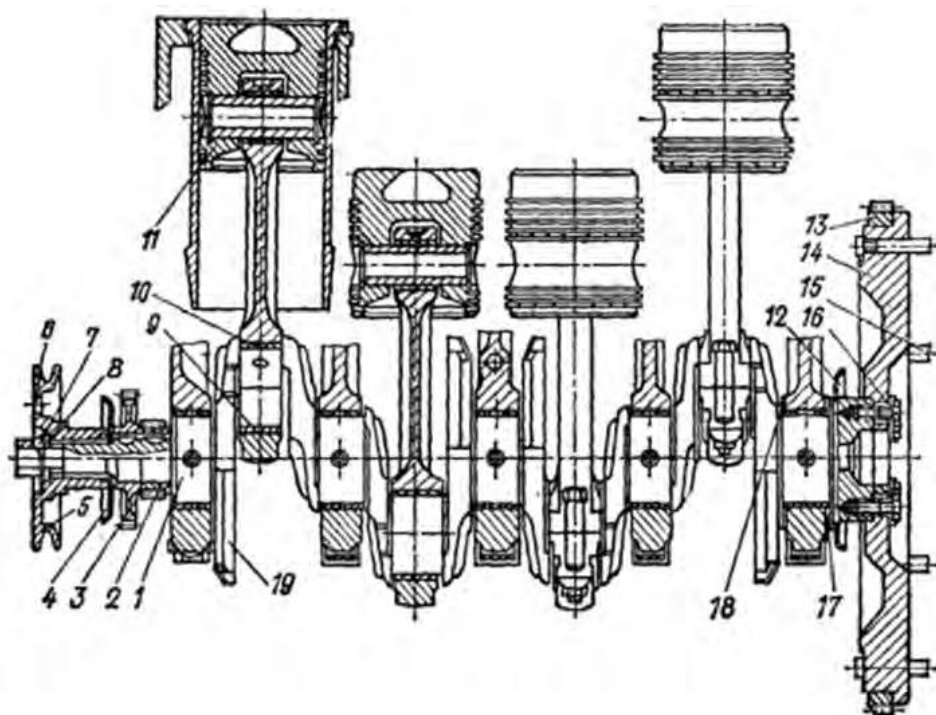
Кривошипно-шатунный механизм двигателя Д-240:
